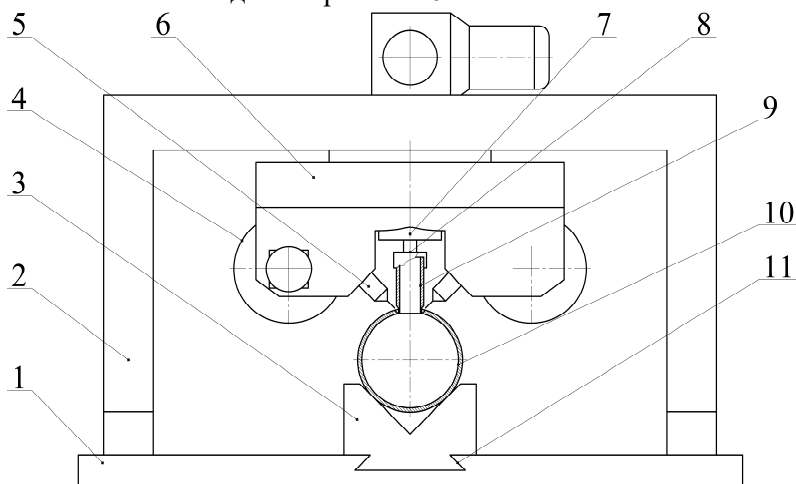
Установка для механизированной прецизионной сварки коллекторов
